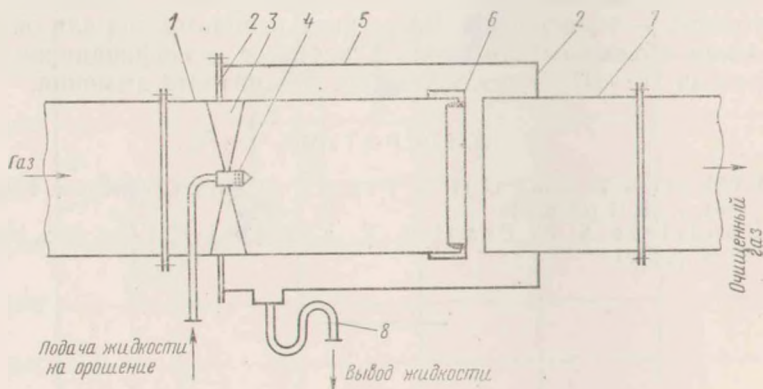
Центробежный сепаратор для мокрой очистки газа:
